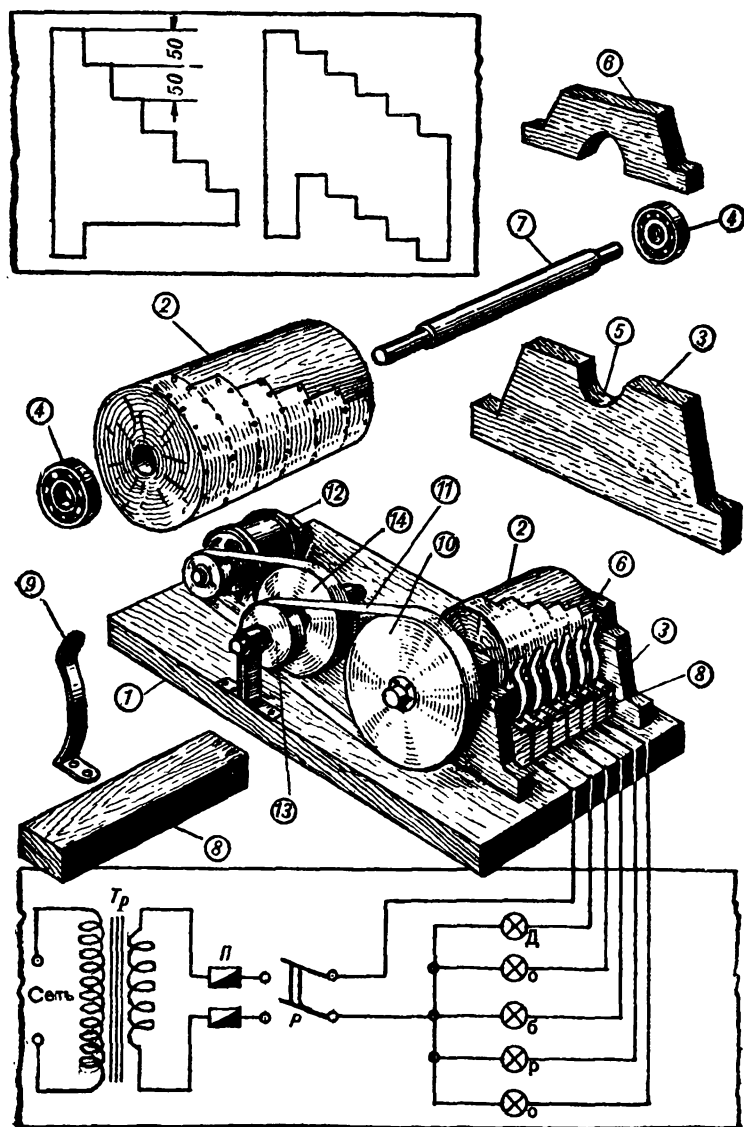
Самодельный контактор и его детали: Тр — понижающий трансформатор; П — предохранители; Р — рубильник.
